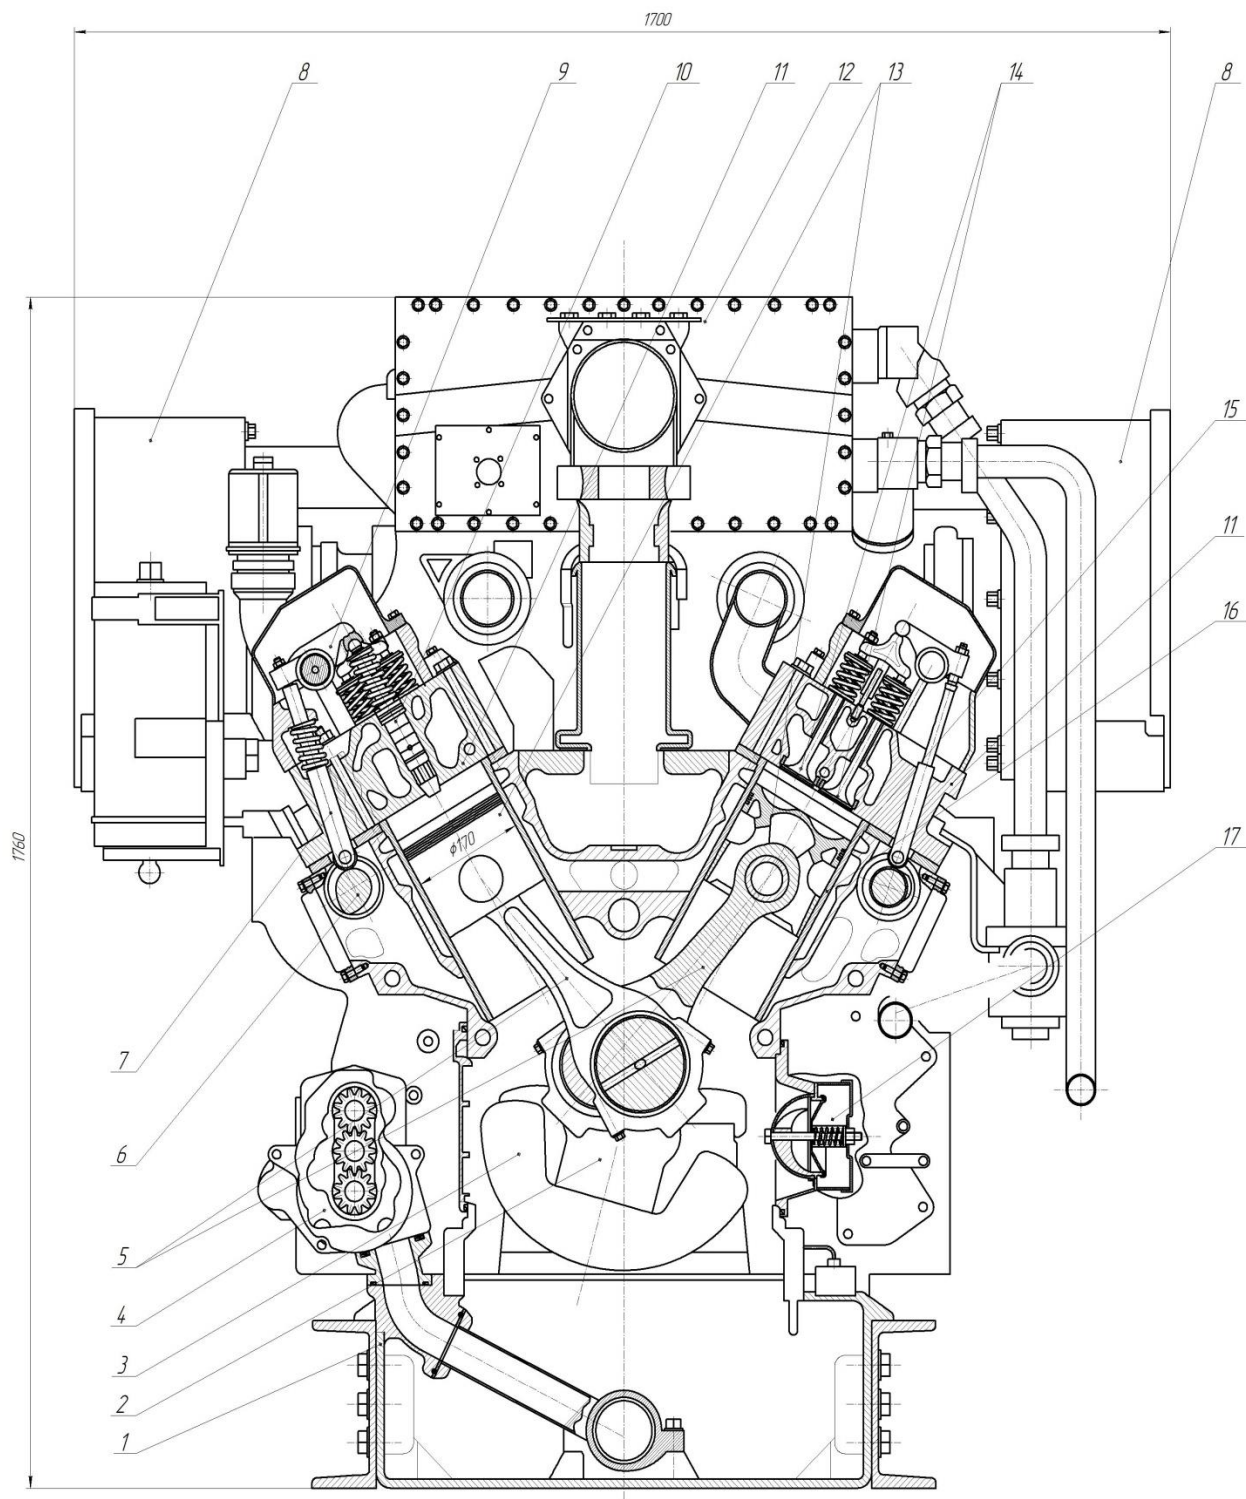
Головний двигун CAT 3512C: 1 – картер; 2 – колінчастий вал; 3 – противага; 4 – масляний насос; 5 – шатуни; 6 – вал кулачковий; 7 – штанги; 8 – ГТН; 9 – коромисло; 10 – насос-форсунка; 11 – головка циліндра; 12 – охолоджувач повітря наддуву; 13 – поршні; 14 – клапани випускні; 15 – поршневі кільця; 16 – циліндрова втулка; 17 – клапан запобіжний
